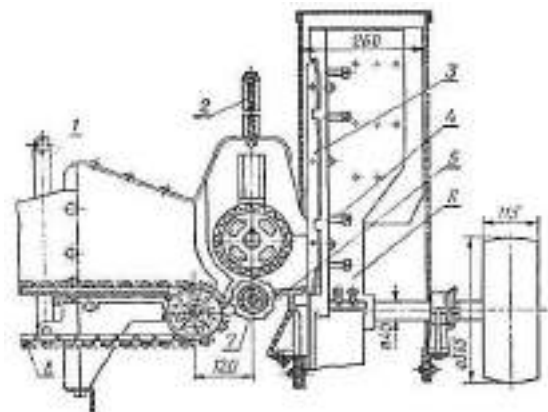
Соломосилосорізка РСС-6: 1 - скоба керування; 2 - пружина; 3 - ніж; 4 - регульовальні гвинти; 5 - протиріжуча пластина; 6 - лопать; 7 - нижній живильний валець; 8 - транспортер.
